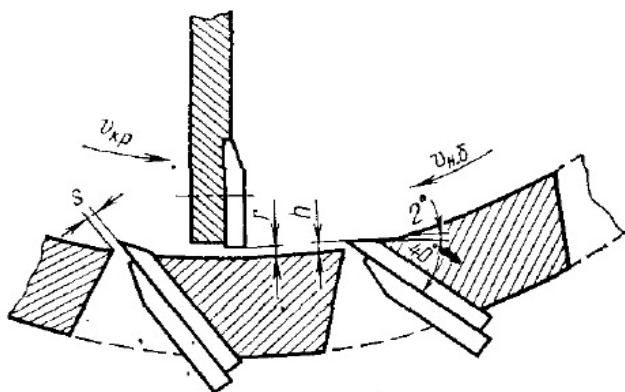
Схема узла резания центробежных стружечных станков [2]
